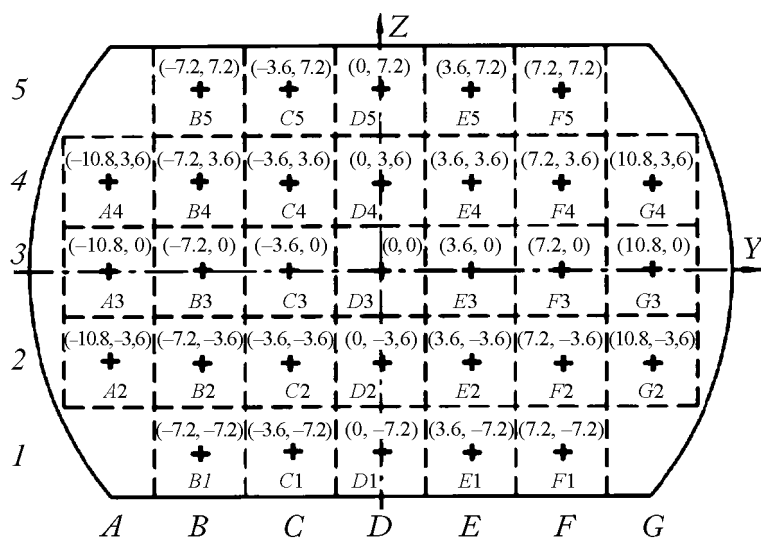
Схема порезки заготовки в продольном направлении и карта микрообразцов для испытаний на растяжение
